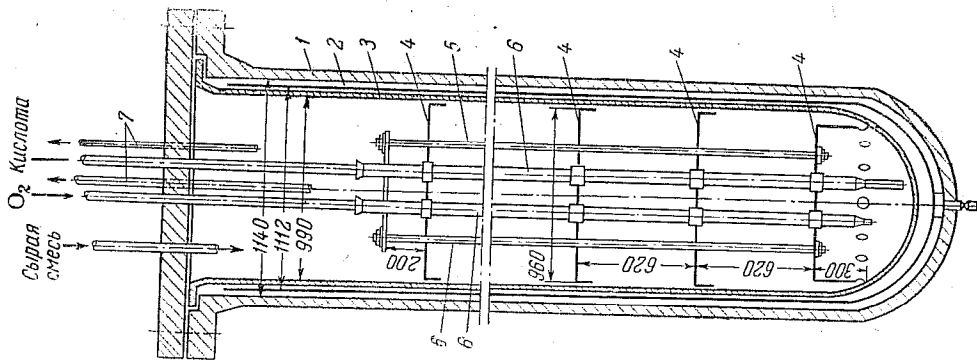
Автоклав непрерывного действия с ситчатыми тарелками: 1—корпус; 2—защитный стакан; 3—реакционный стакан; 4—ситчатые тарелки; 5—распорные штанги; 6—каналы; 7—перфорированные трубы.
